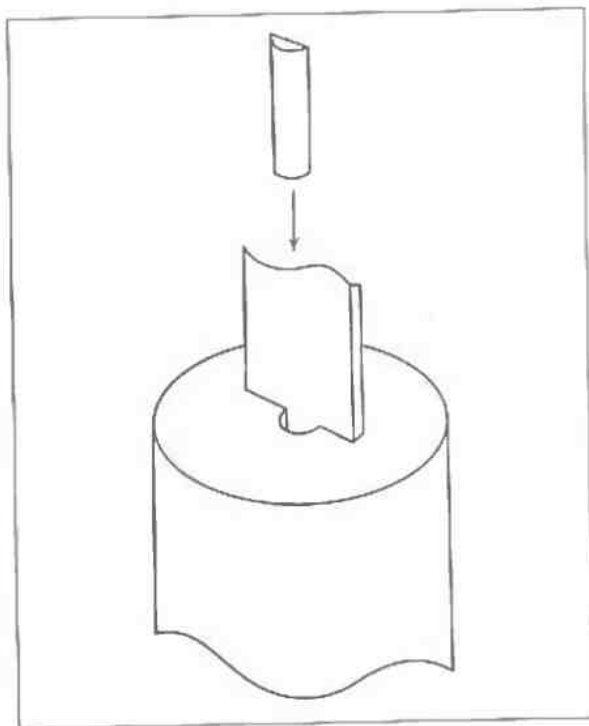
Заделка отверстий в заготовке рукоятки фасонными вставками
